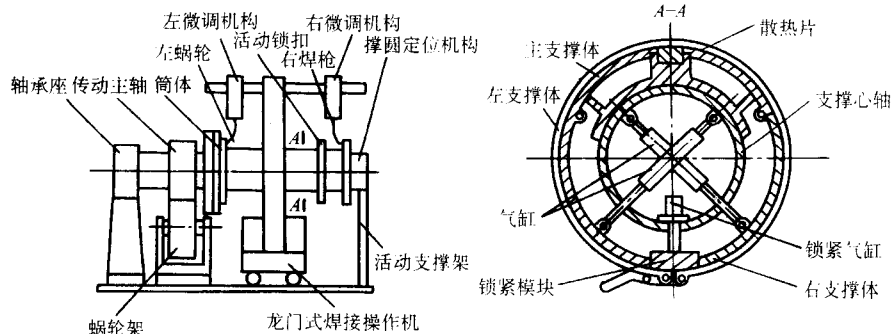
超薄壁长筒体自动焊接装置的结构和工作原理示意图
